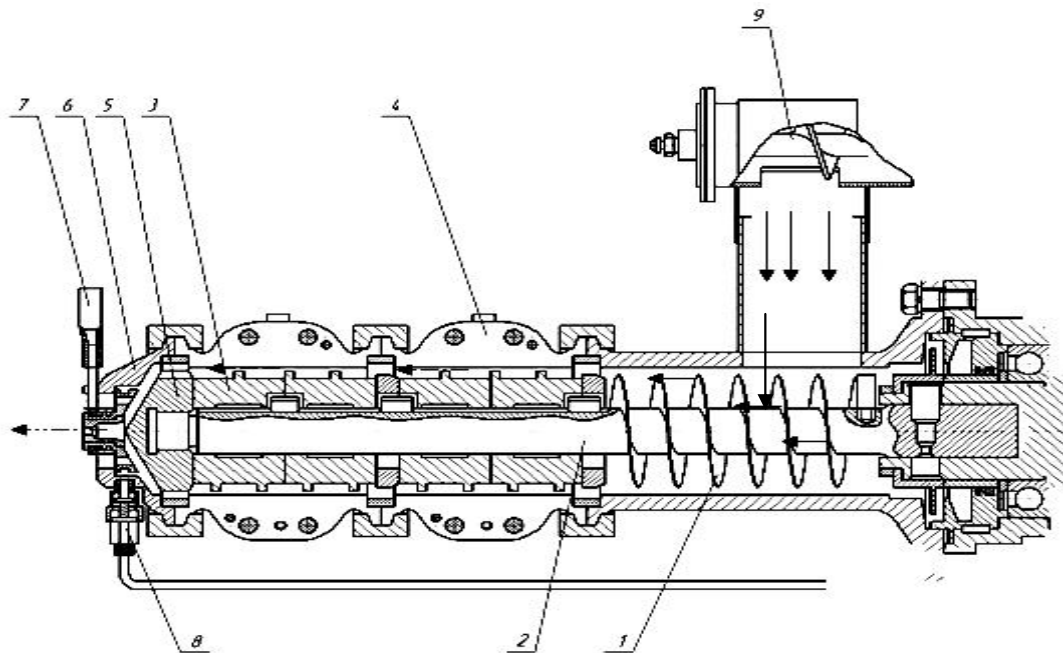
Конструктивно-технологическая схема пресс-экструдера для приготовления кормосмеси на основе измельченной соломы: 1 – подающий шнек; 2 – вал ротора; 3 – шнековая часть; 4 – корпус; 5 – коническая головка; 6 – регулятор гранулятора; 7 – рычаг регулятора гранулятора; 8 – термомпара; 9 - дозатор
